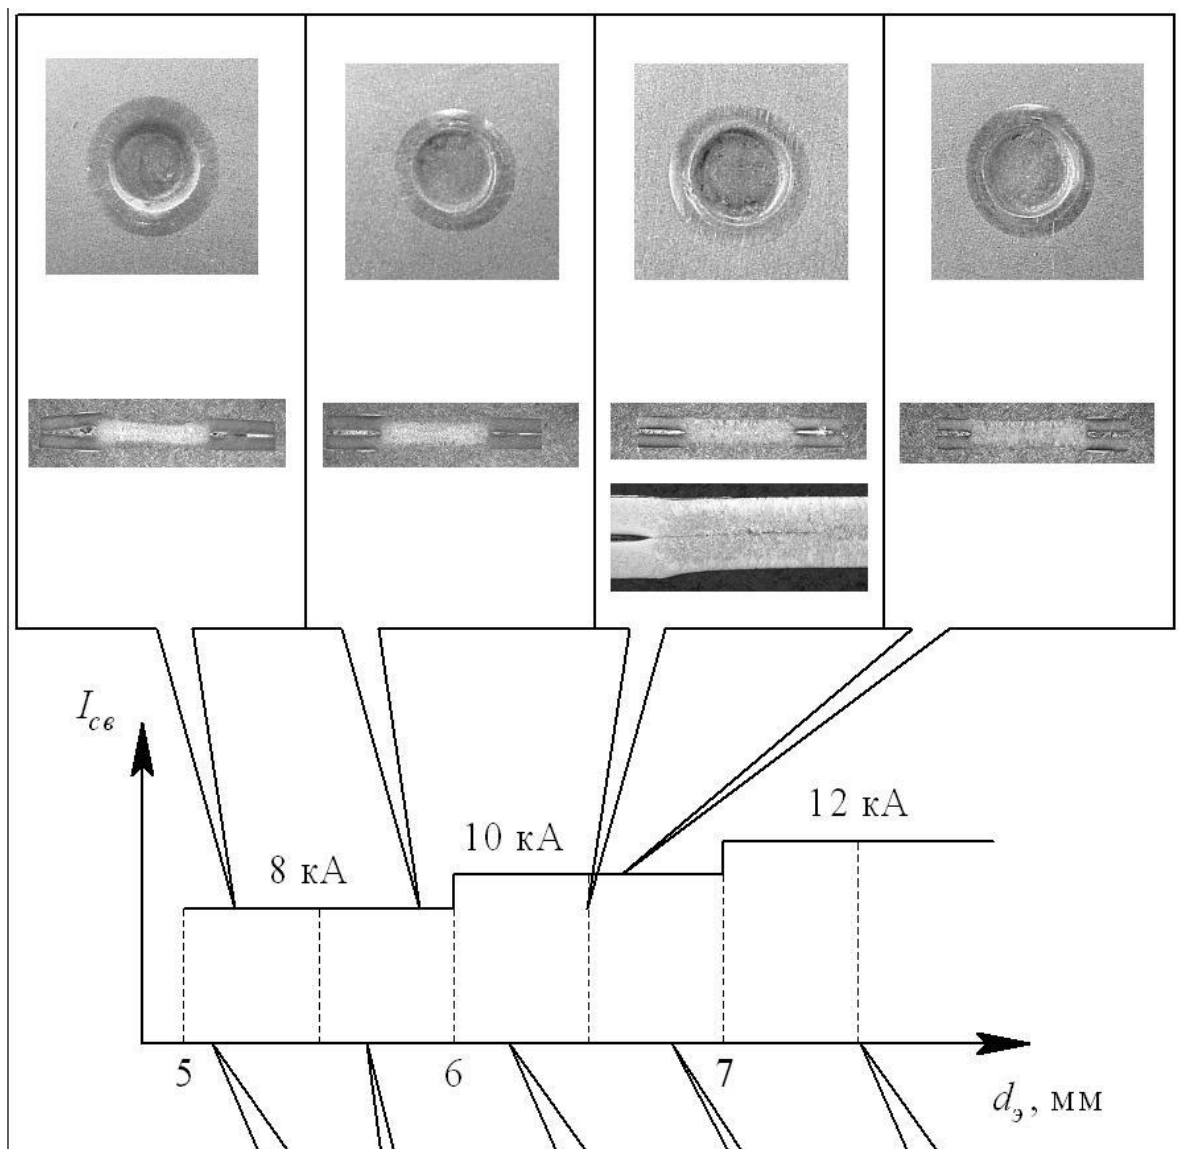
Влияния износа сварочных электродов на качество контактной сварки в условиях ступенчатого увеличения сварочного тока 1+1 мм, сталь 08Ю
